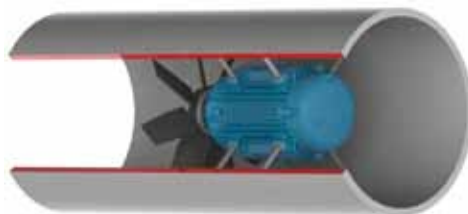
Befestigungsdarstellung des Motors in einem Entlüftungsrohr
